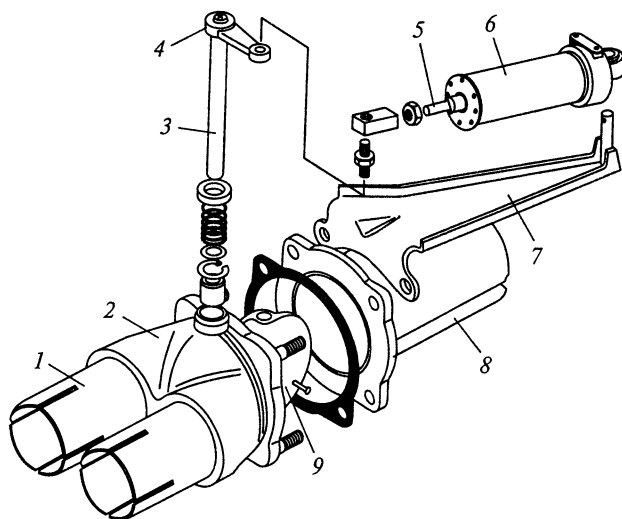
Моторный тормоз-замедлитель грузовых автомобилей ЗИЛ:
